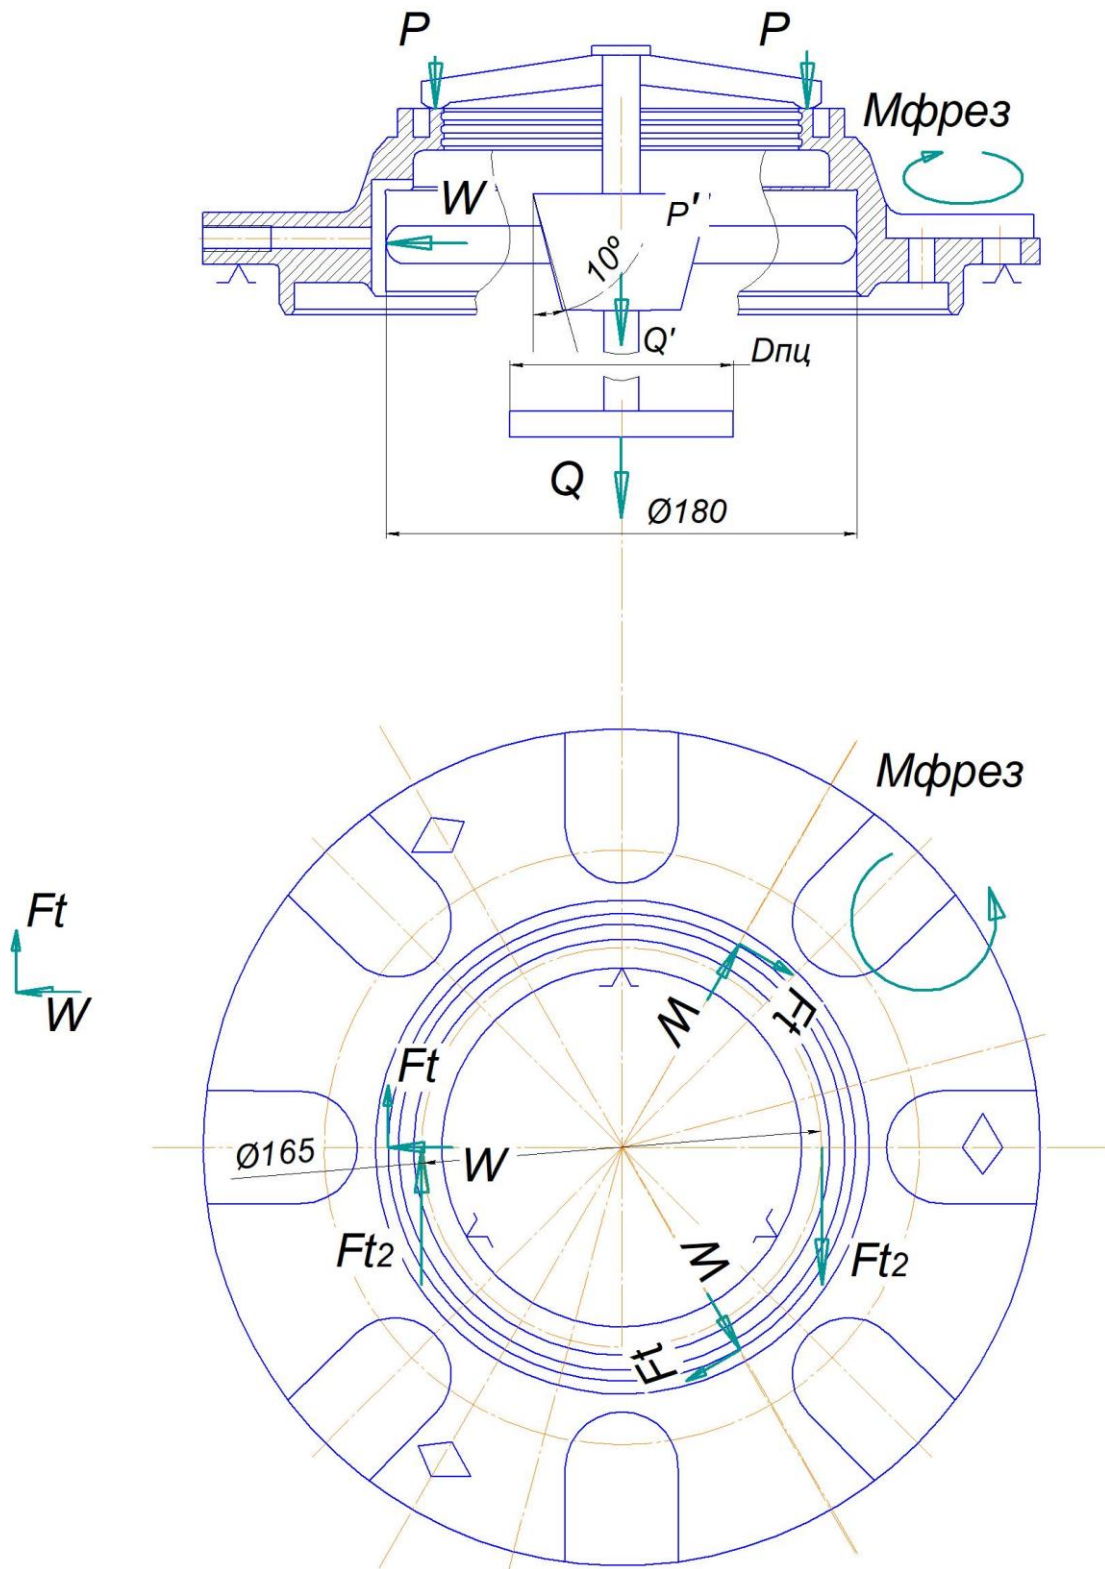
Розрахункова схема фрезерно-свердлильного пристрою
